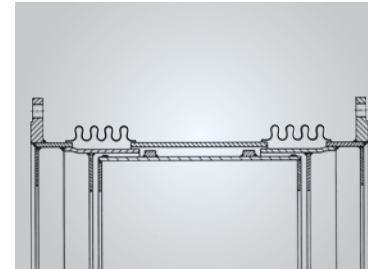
Universal-Kompensator für eine Heißwindleitung DN 2500
